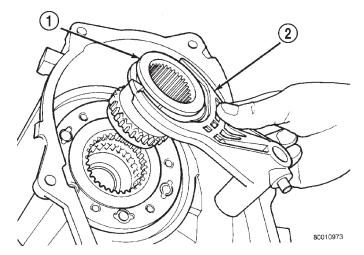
Desmontaje del manguito y de la horquilla de escala de posiciones
